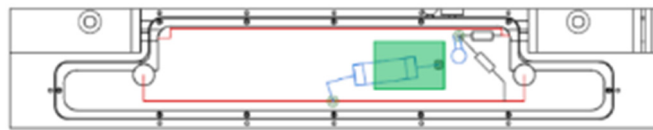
AFAS-B Top Fork 及び Bottom Fork 検出器のアンプ配置図
